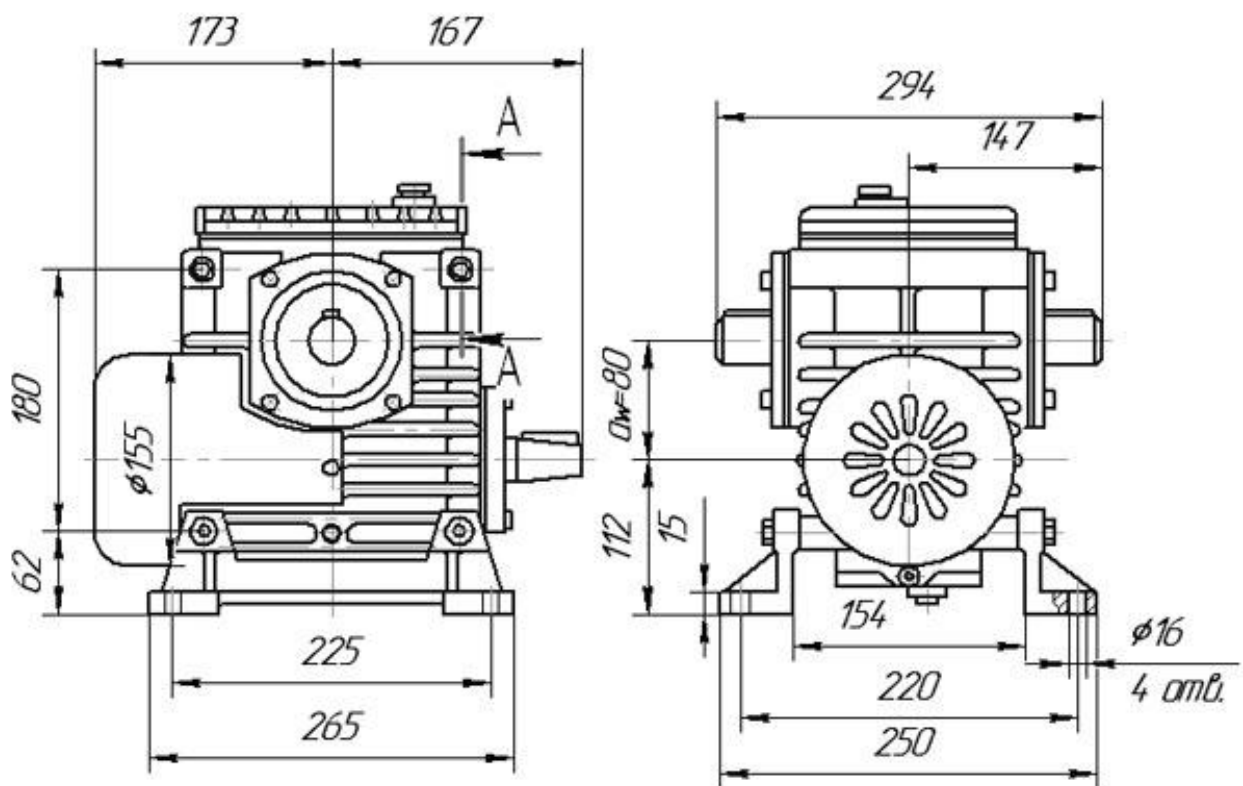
Черв'ячний редуктор універсального типу Ч80
